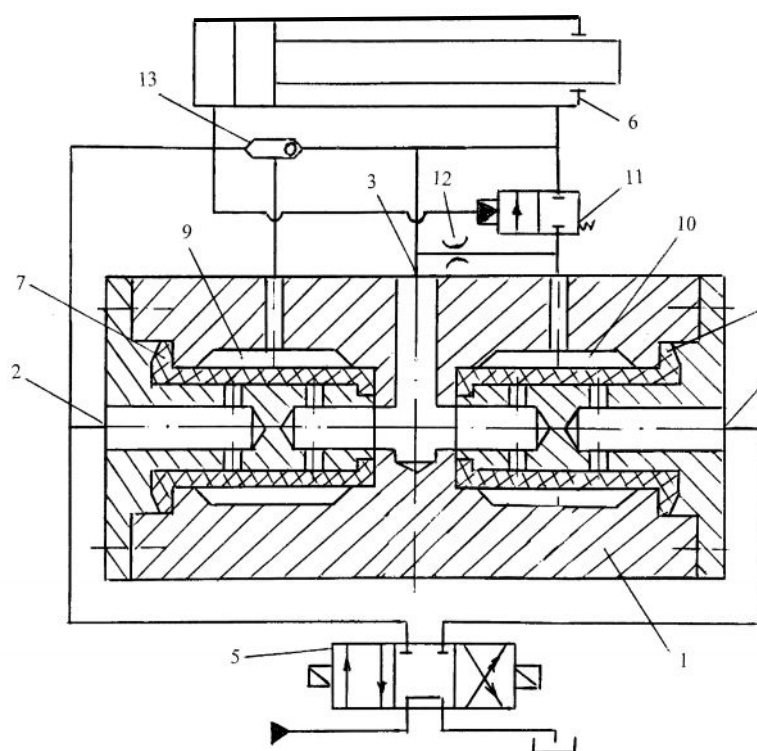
Конструктивное исполнение основного каскада преобразователя скорости перемещения штока гидроцилиндра с цилиндрическими мембранными запорно-регулирующими элементами
